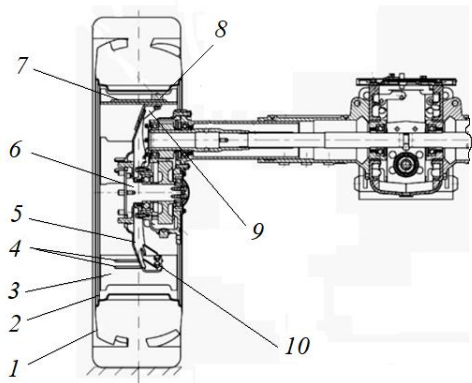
Механизм для бесступенчатой регулировки колеи колес
